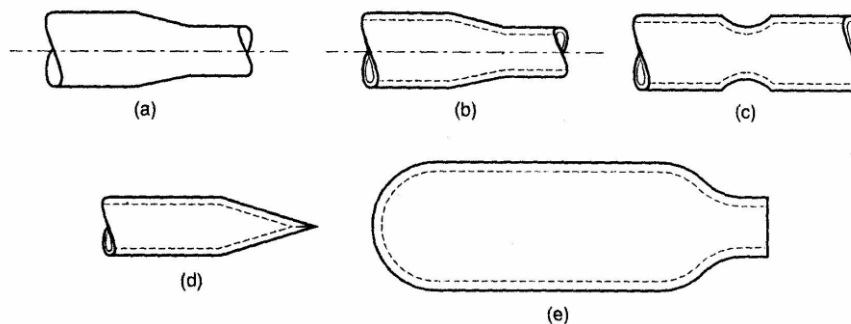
Ejemplos de partes hechas por estampado (a) reducción de material sólido, (b) ahusado de un tubo, (c) estampado para formar un canal en un tubo, (d) afilado de un tubo y (e) estampado del cuello en un cilindro de gas.
